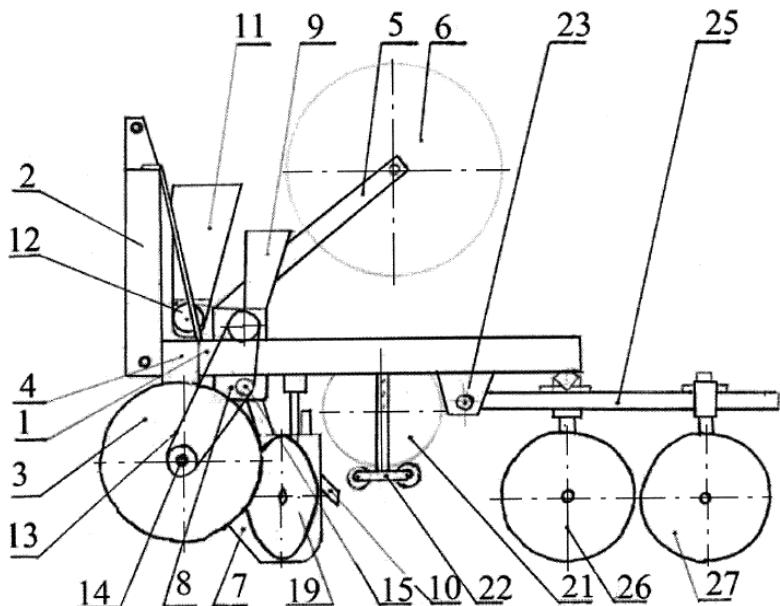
Устройство для укладки пленки: 1-рама; 2, 15-приспособление; 3-опорные элементы в виде колес; 4-вертикальные стойки; 5-держатель; 6-бобина с капельной лентой; 7-сошник; 8-вакуумный высыпающий аппарат; 9-бункер; 10-направляющий канал для капельной ленты; 11-бункер; 12-дозатор; 13-цепной привод; 14-вал; 16-квадраты; 17-держатель; 18-телескопические стойки; 19-дисковый нож; 20-горизонтальный ролик; 21-рулон; 22-держатель; 23-кронштейн; 24-вал; 25-навеска; 26-прикатывающий ролик; 27-дисковый нож; 28-квадраты
